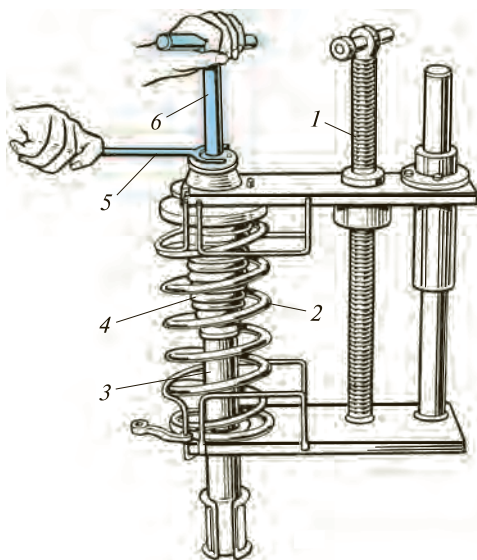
Установка телескопической стойки в приспособление для разборки:
